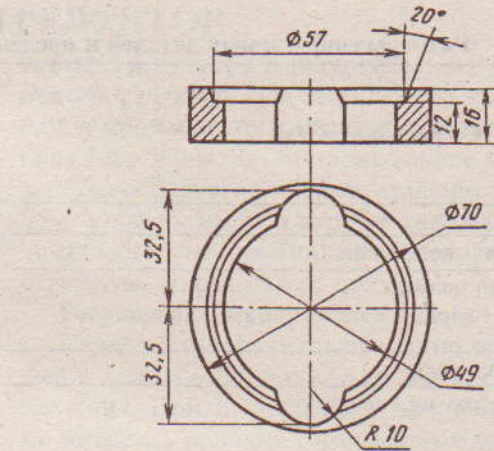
Оправка для выпрессовки корпуса и грязезащитного кольца
